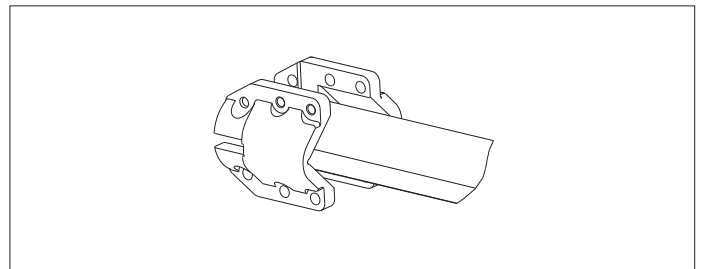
Установка двух полумуфт на вал квадратного сечения
